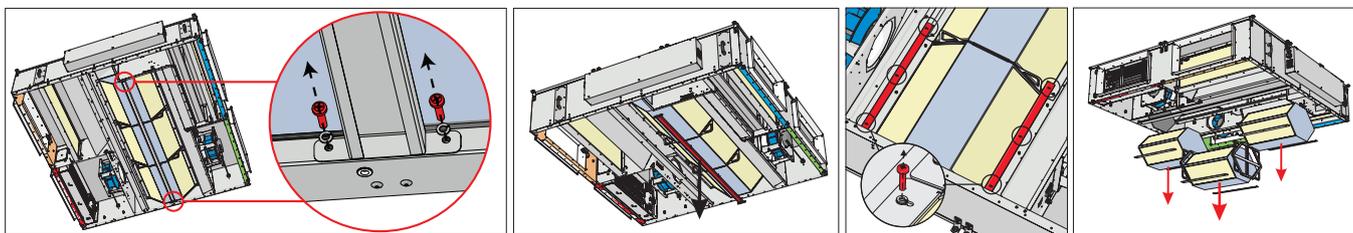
La version en installation au plafond d'AmberAir Compact CX P
